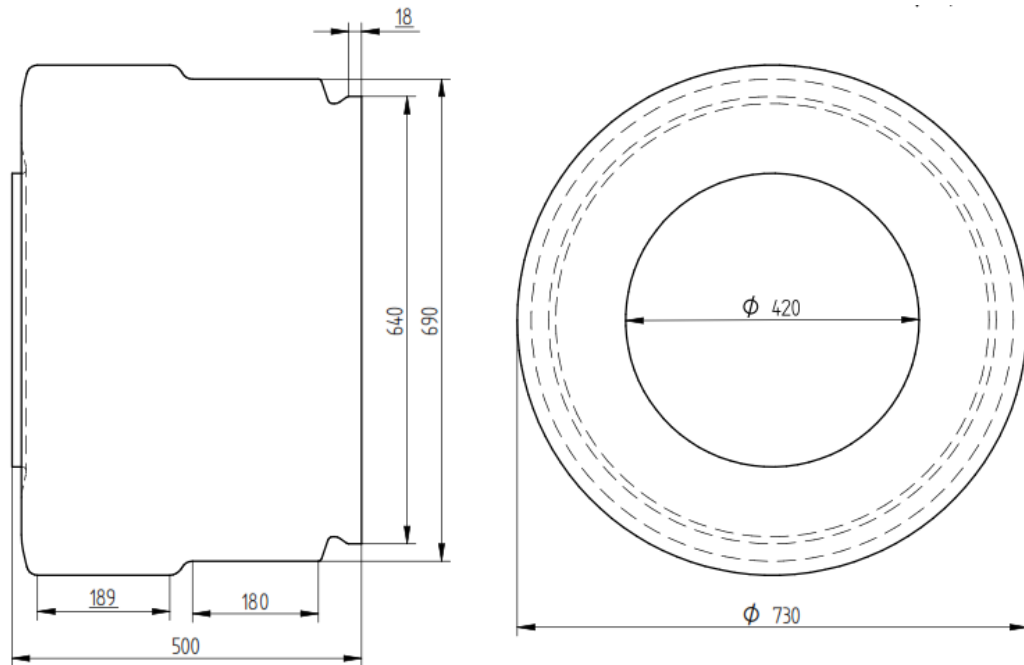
Vistas del tambor rotativo Fuente: Autor
